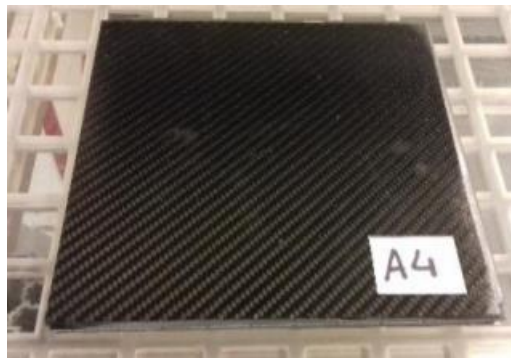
Laminado A4. Ensaio balístico n.º3.
